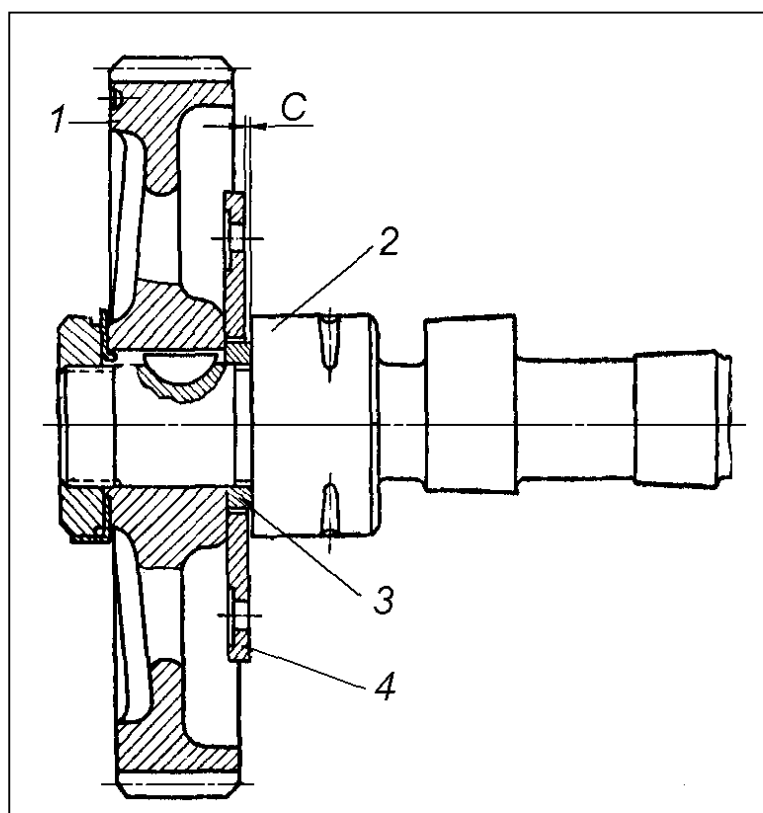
К контролю осевого зазора в упорном подшипнике распределительного вала:
